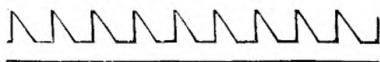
Guttapercha-Rinnen für Plattenkasten.
